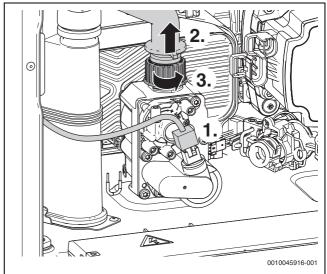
Smontaggio del flessibile di collegamento gas, del giunto ad innesto e del dado
